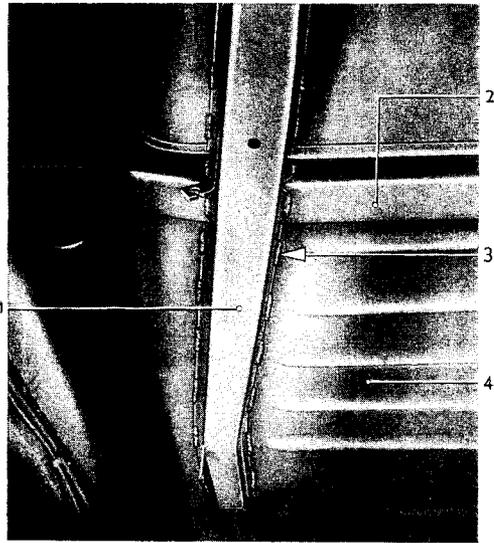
Linker Vorderrahmenlängsträger an Bodenblech und hinteren Motorquerträger zusätzlich lichtbogengeschweißt – Rechten Längsträger in gleicher Weise lichtbogenschweißen
